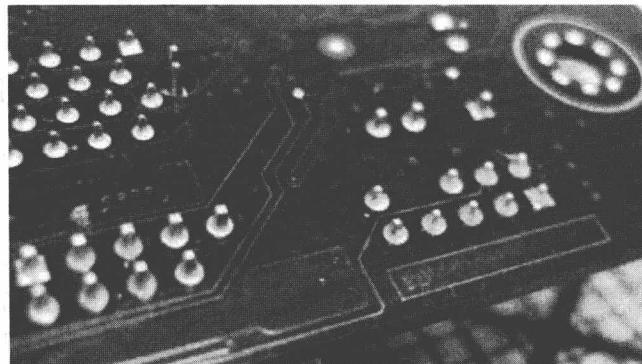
PCB 实现元器件的布线、电气连接、电绝缘
